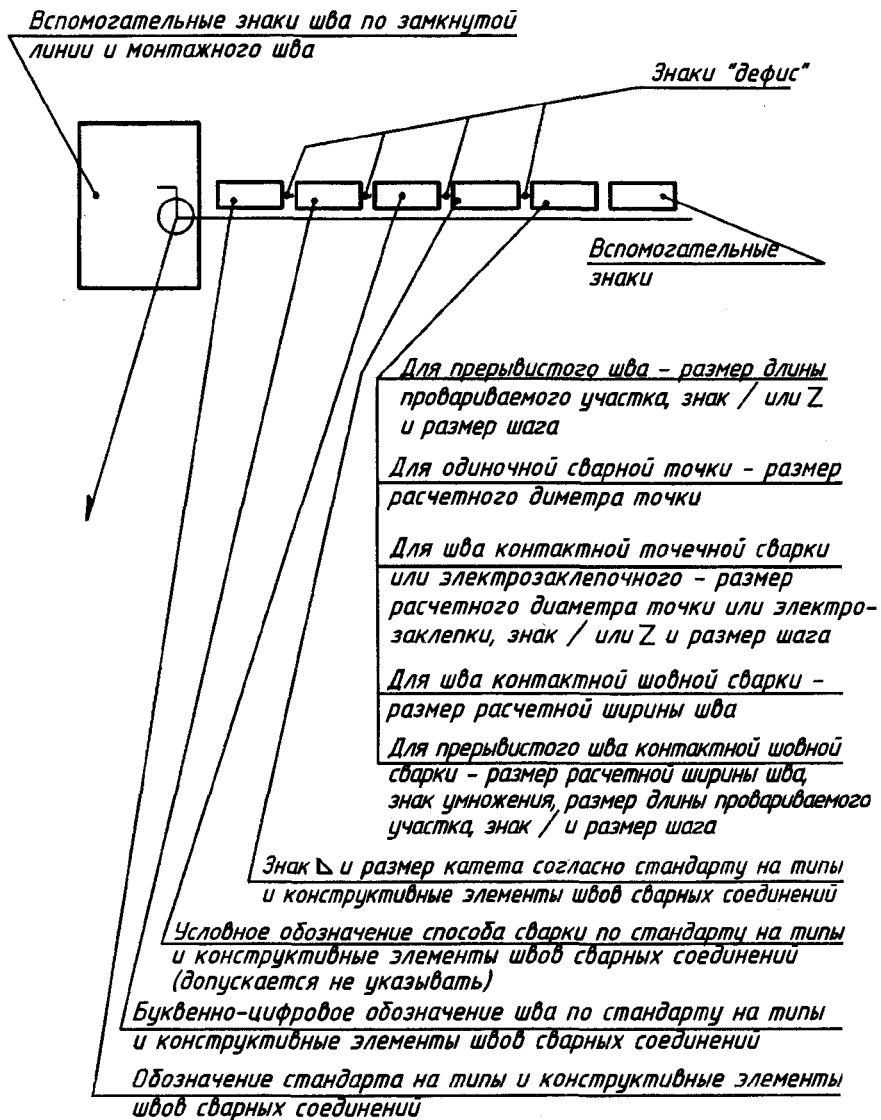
Структура условного обозначения стандартного сварного шва или одиночной сварной точки
